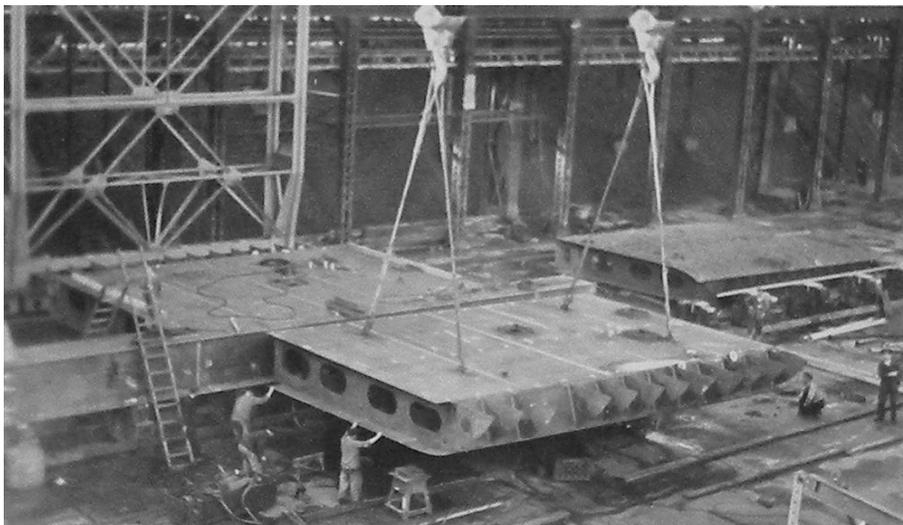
Montage d'un élément du double fond qui arrive latéralement
